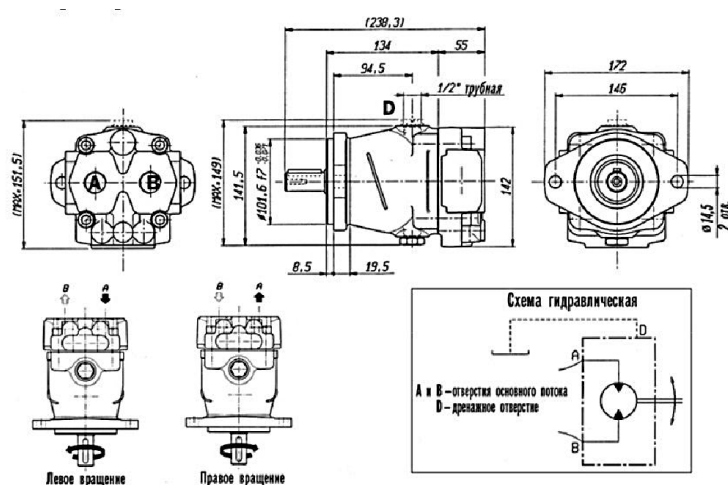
Габаритные и присоединительные размеры гидромоторов типа М2
